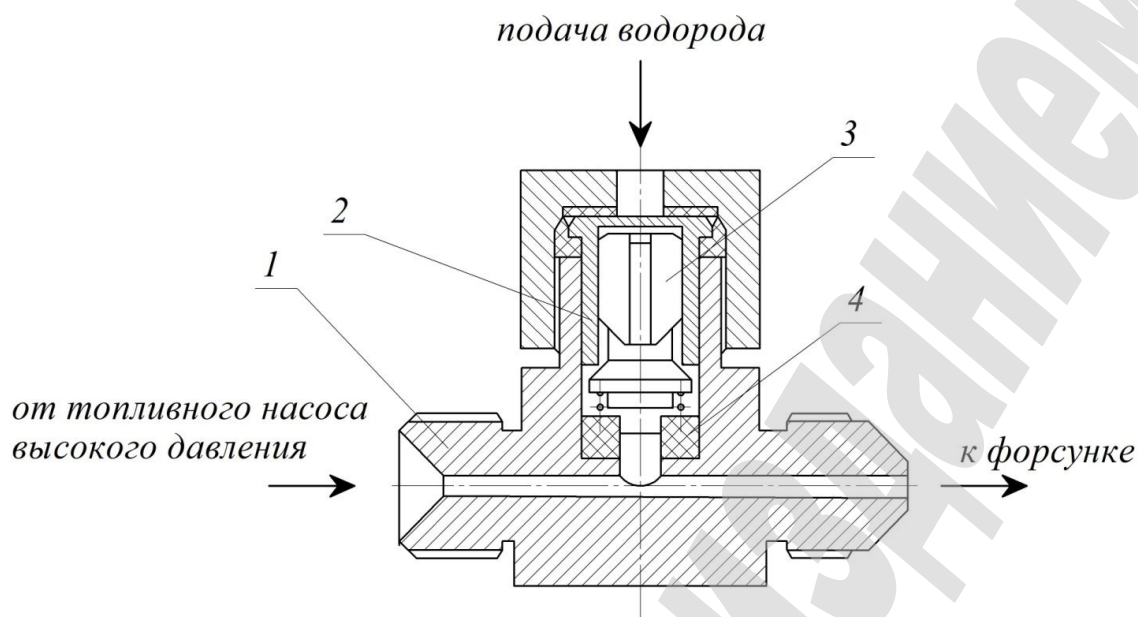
Устройство для подачи водорода в линию высокого давления: 1 – корпус тройника; 2 – корпус размещения клапана; 3 – невозвратный клапан с направляющим хвостовиком; 4 – ограничитель хода клапана
